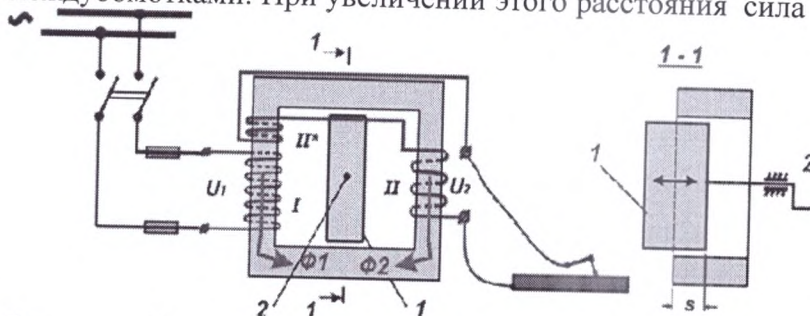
Схема сварочного трансформаторов типа СТАН. I – первичная обмотка; II – вторичная обмотка основная; II* – вторичная обмотка реактивная;
